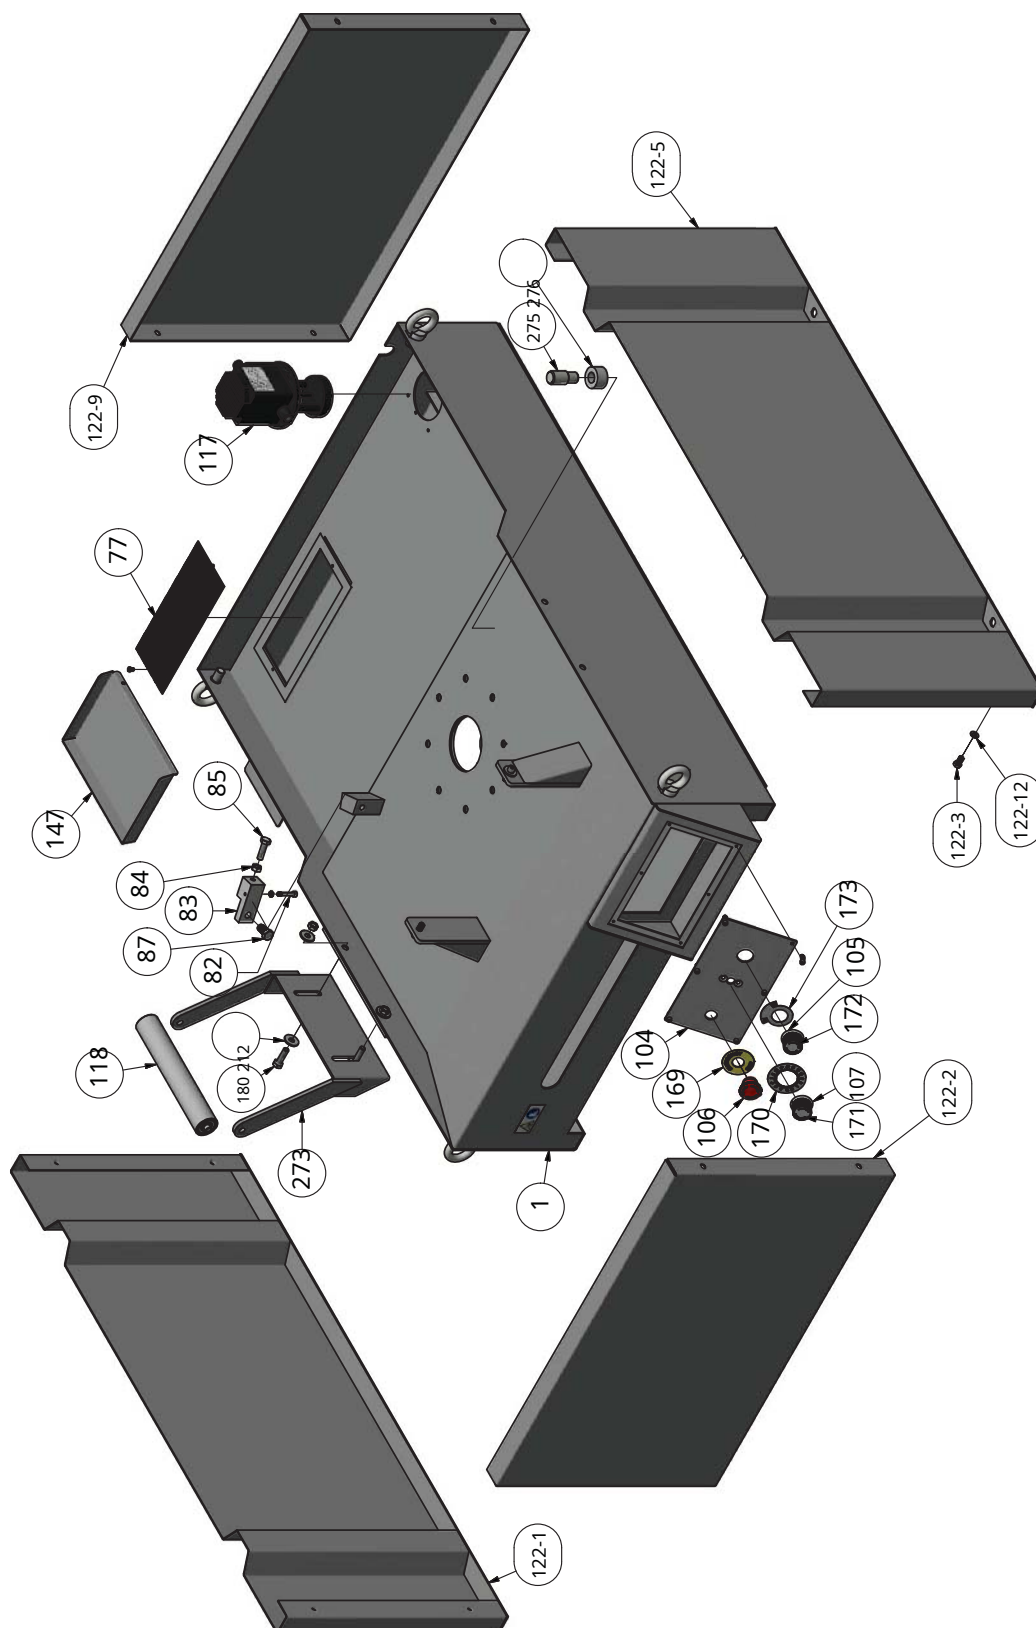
Explosionszeichnung - Dibujo de piezas de repuesto
